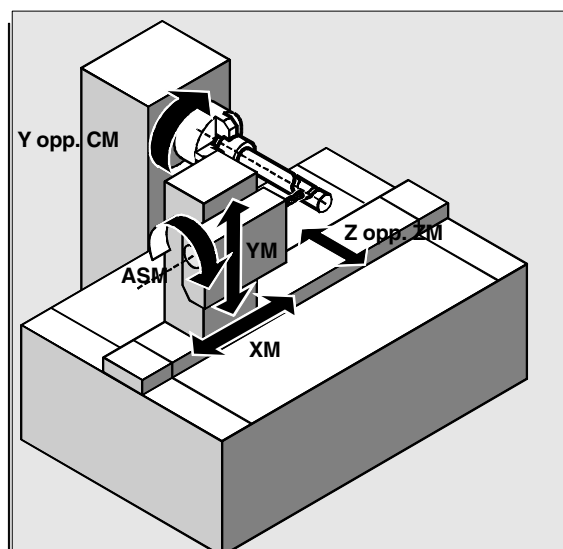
Cinematica di macchina con asse Y (YM) di macchina
